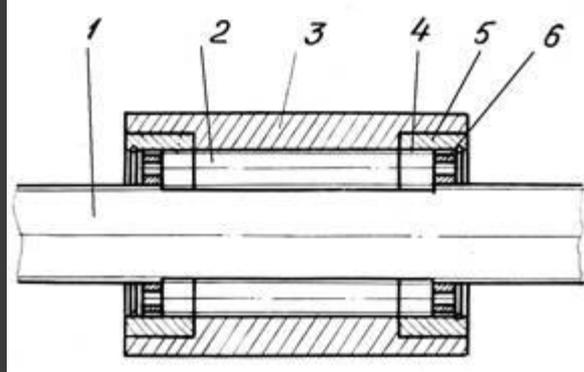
Планетарная передача винт – гайка с короткими резьбовыми роликами:
